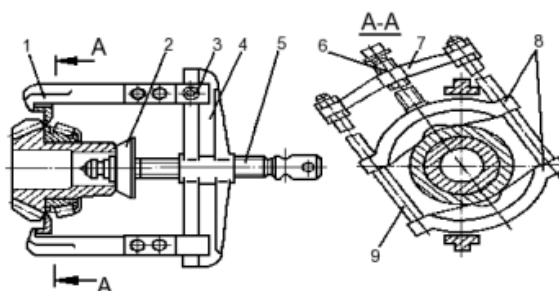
Съемник внутренних колец подшипников ведущих зубчатых колес и чашек дифференциала моста 1 – захват; 2 – наконечник; 3, 5, 6 – винты; 4, 7 – траверсы; 8 – клин; 9 – стойка
